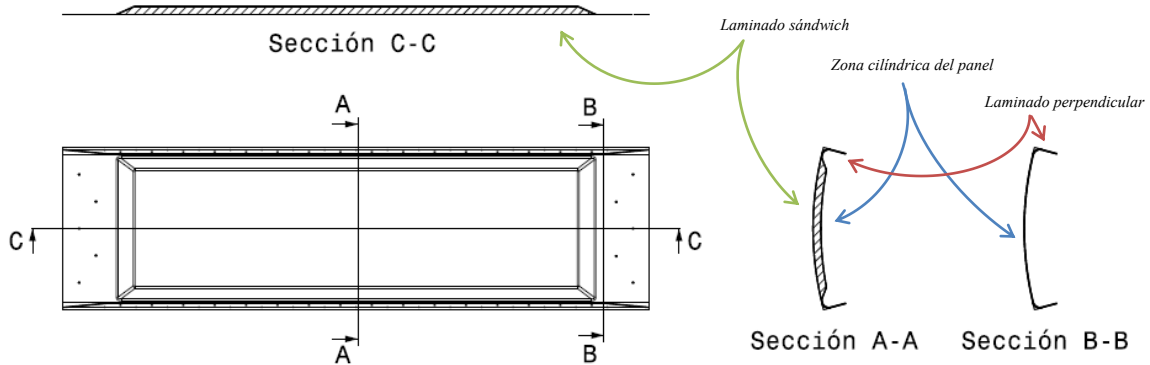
descripción geométrica del panel cilíndrico diseñado.
